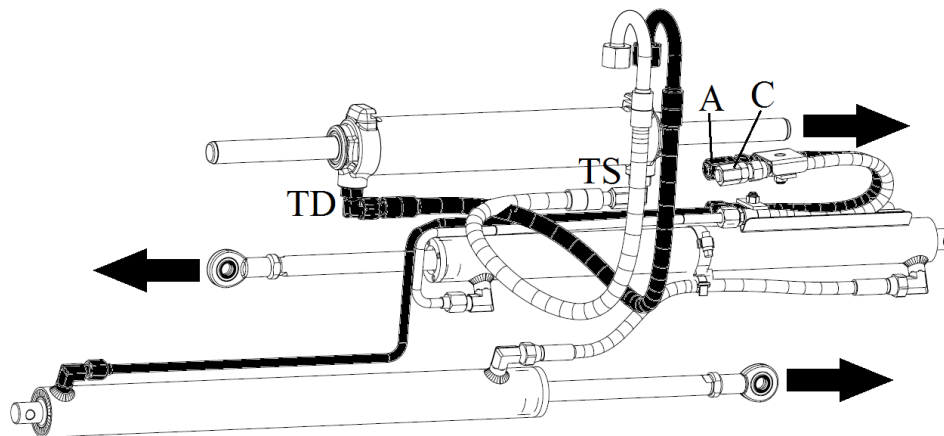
Hydraulische Anlage für die Ausführungen mit separatem Seitenschub und mit Position der Zinkenversorgungseingänge im Inneren des Rahmens.
